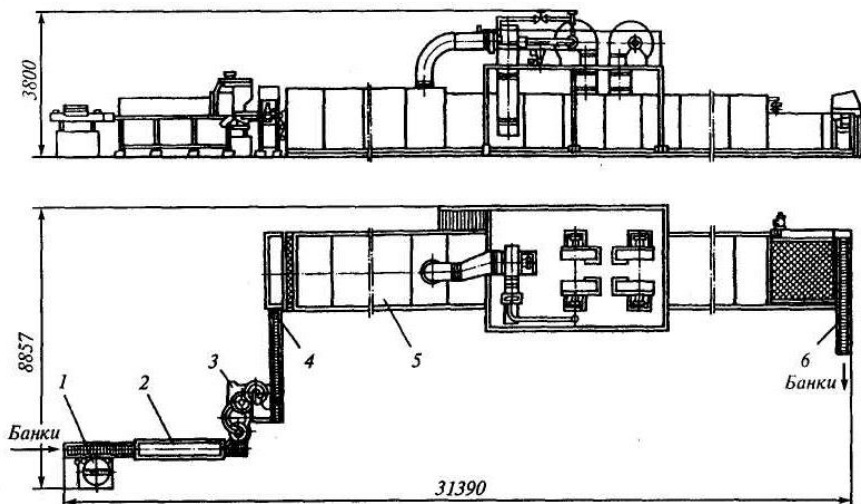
Установка А2-КПО: 1 – наповнювач банок; 2 – ексгаустер; 3 – закупорювальна машина; 4 – подаючий конвеєр; 5 – пастеризатор-охолоджувач; 6 – вивантажувальний конвеєр.
